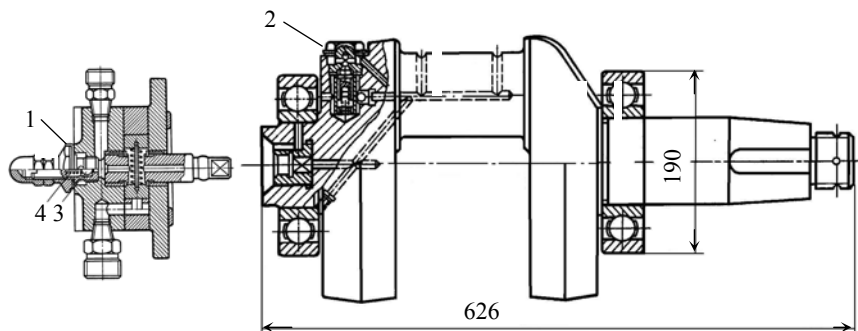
Масляный насос и коленчатый вал компрессора КТ6 (КТ7):
